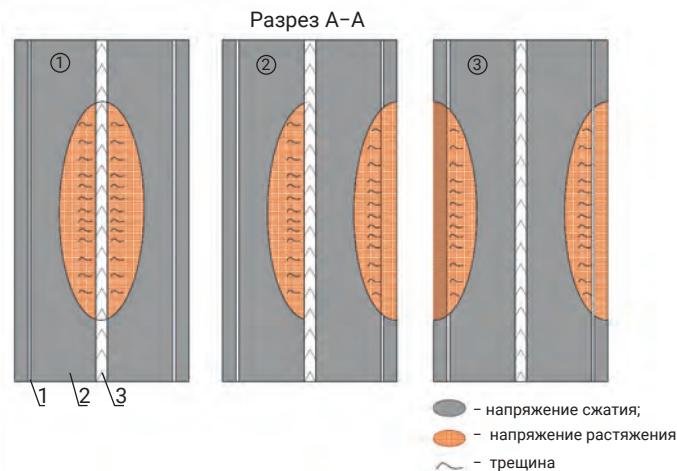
Условия образования трещин в сварных швах и в деталях конструкции; 1 – стенка блока, 2 – нижний пояс, 3 – продольный шов
